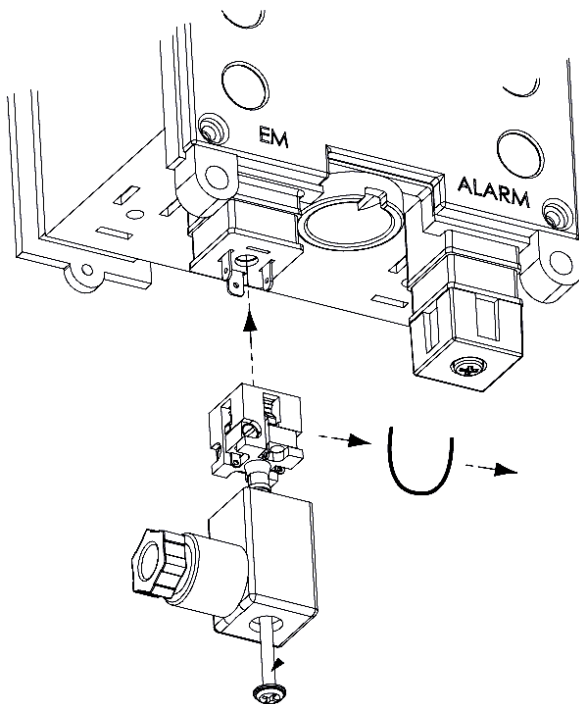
DIN-Stecker, Entfernen der Drahtbrücke
